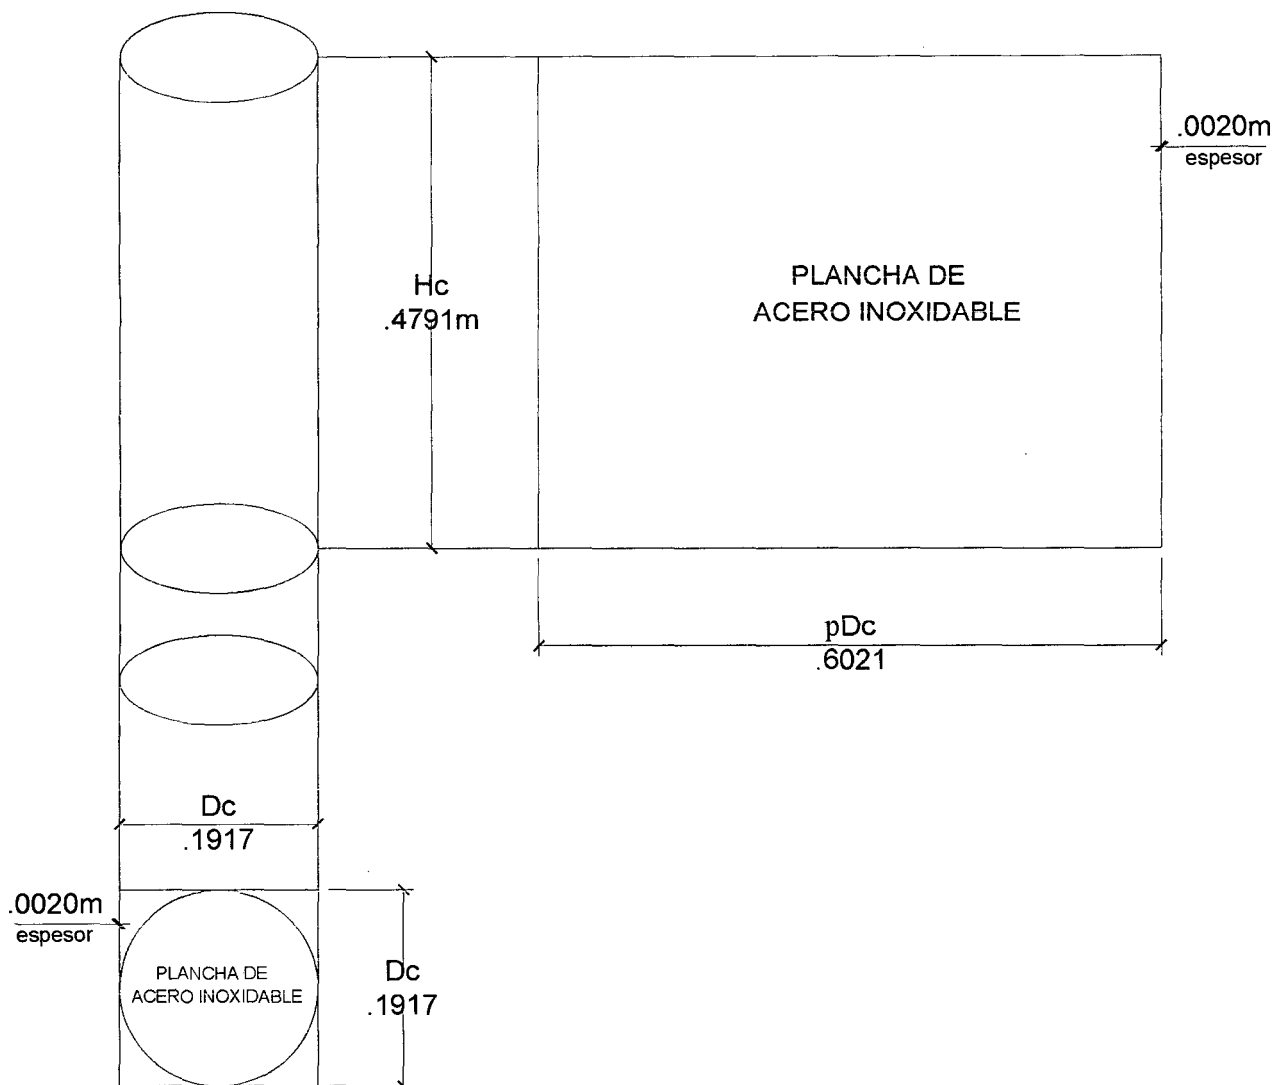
Dimensiones de las planchas de acero para la construcción del cilindro descascarador.
